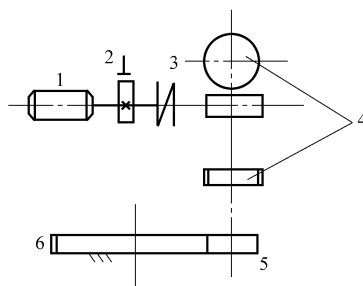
QLD16 型轮胎起重机的回转机构示意图
